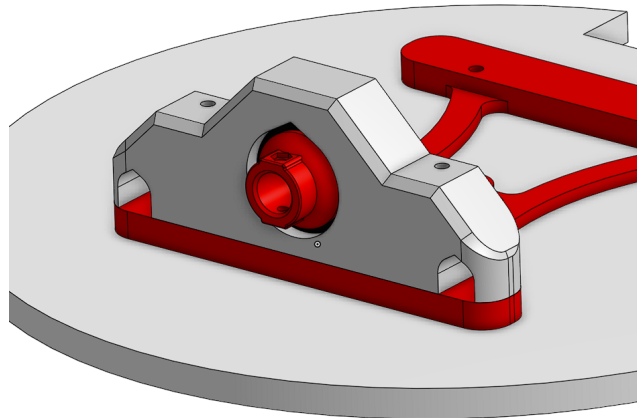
Vista isométrica del ensamblaje de uno de los cojinetes del eje de rotación de la hélice en Onshape [fuente: elaboración propia]
